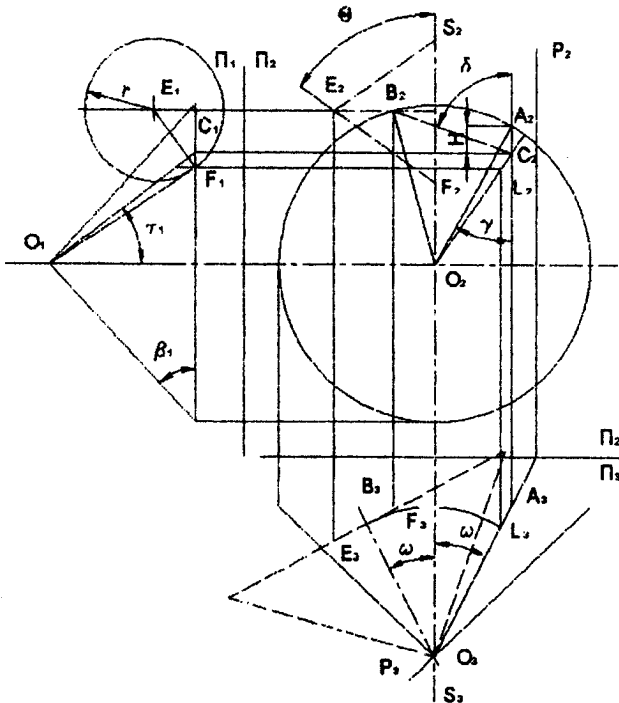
Схема фрезерування зубців з $\gamma \neq 0$ на конічній поверхні
